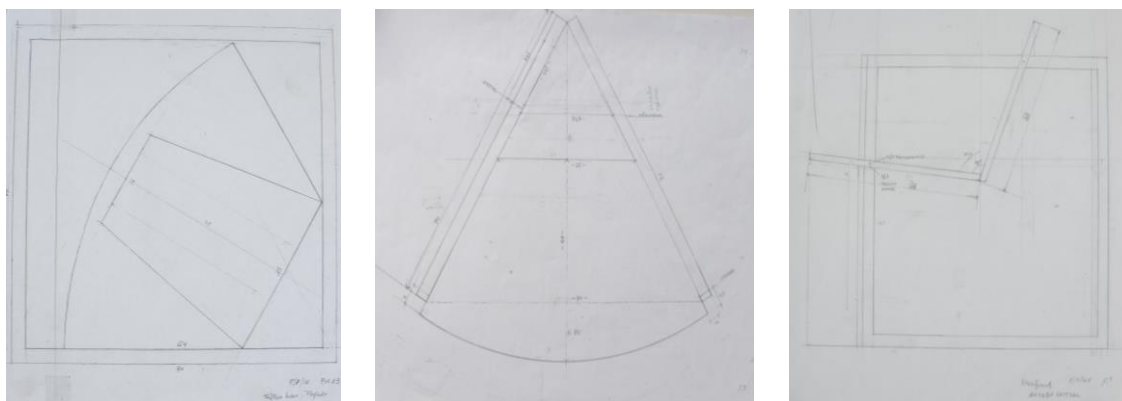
Plano de piezas plegadas, plano de planta y alzado del sillón *Liceo* dibujados a mano por Juan Cuenca para la serie de 2018. Escala 1/3. Archivo personal del autor.
